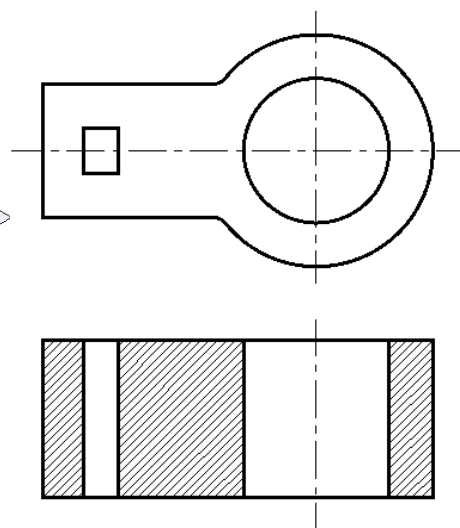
Фронтальный разрез детали и ее вид сверху
